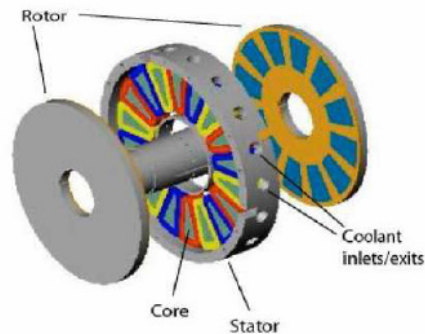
Machine à flux axial un stator et deux rotors avec bobinage sur dents [8]
